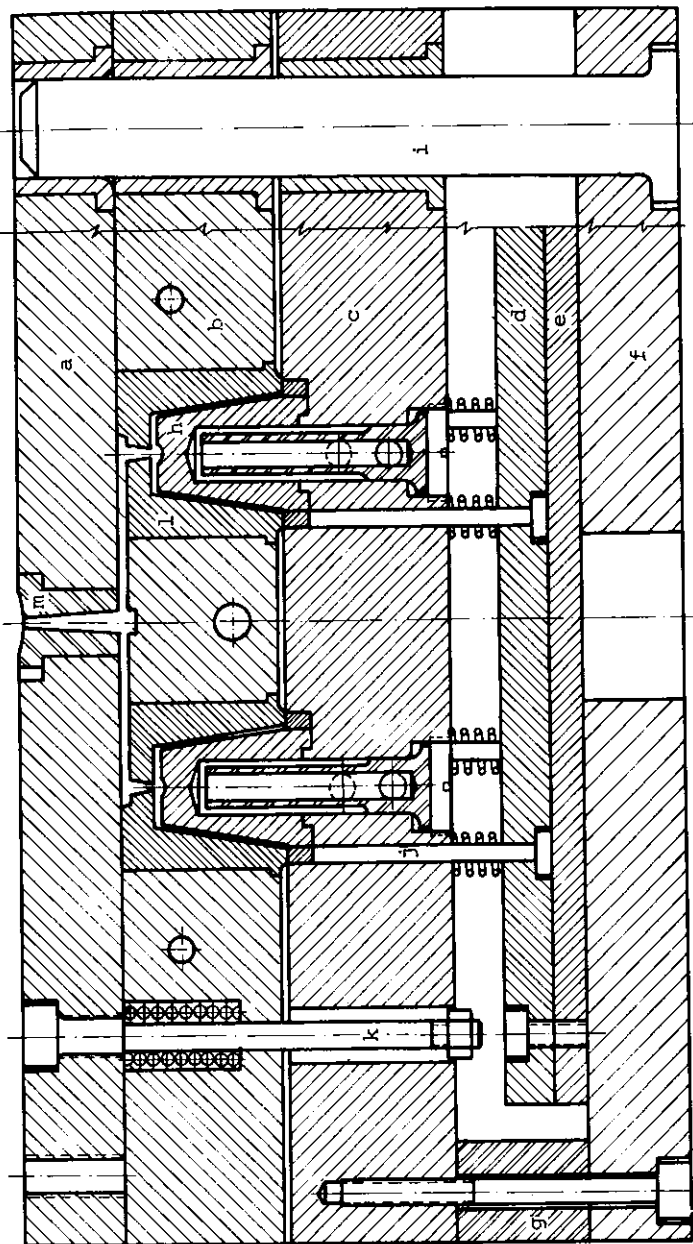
Versão melhorada do projeto da ferramenta. a) Placa de base anterior; b) Placa das cavidades; c) Placa dos machos; d) Contraplaca dos extratores; e) Placa dos extratores; f) Placa de base posterior; g) Bloco separador; h) Machos com sistema de refrigeração; i) Colunas de guia; j) Extratores; k) Limitadores de curso; l) Insertos das cavidades; m) Bucha de injeção.
